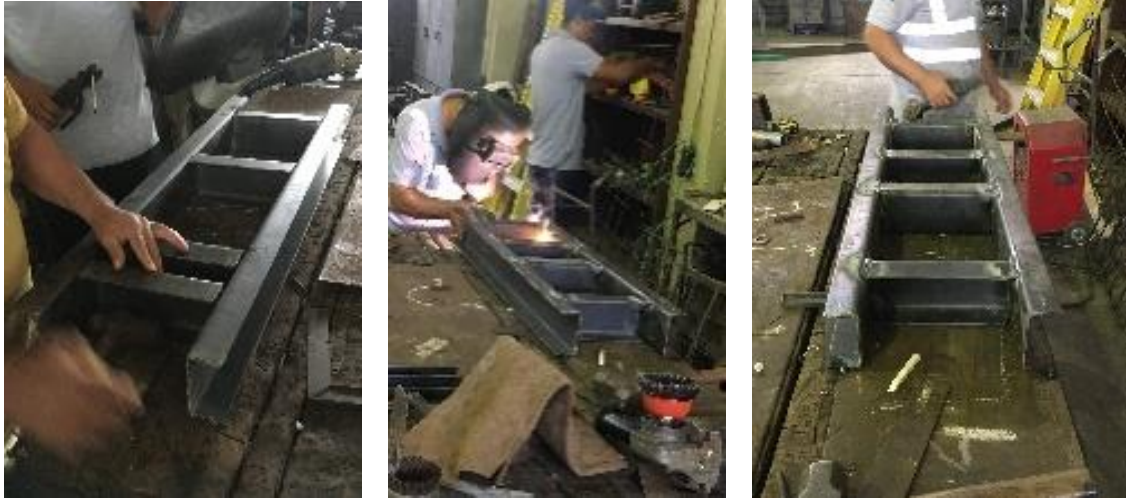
Proceso de corte y soldadura de la base
